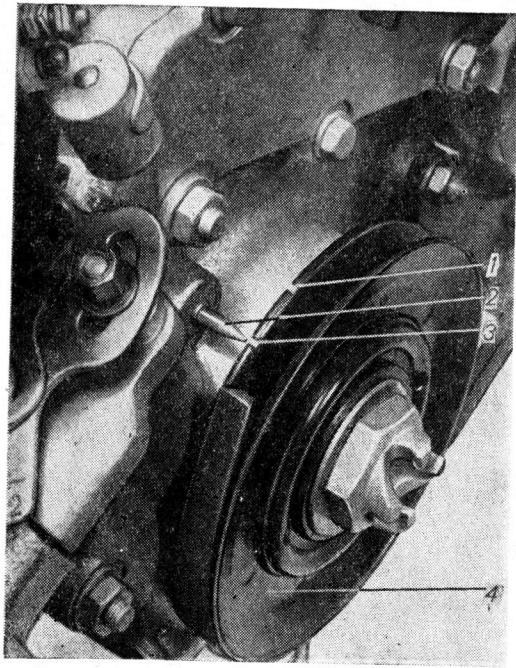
Установочные метки на ободе приводного шкива вентилятора:
